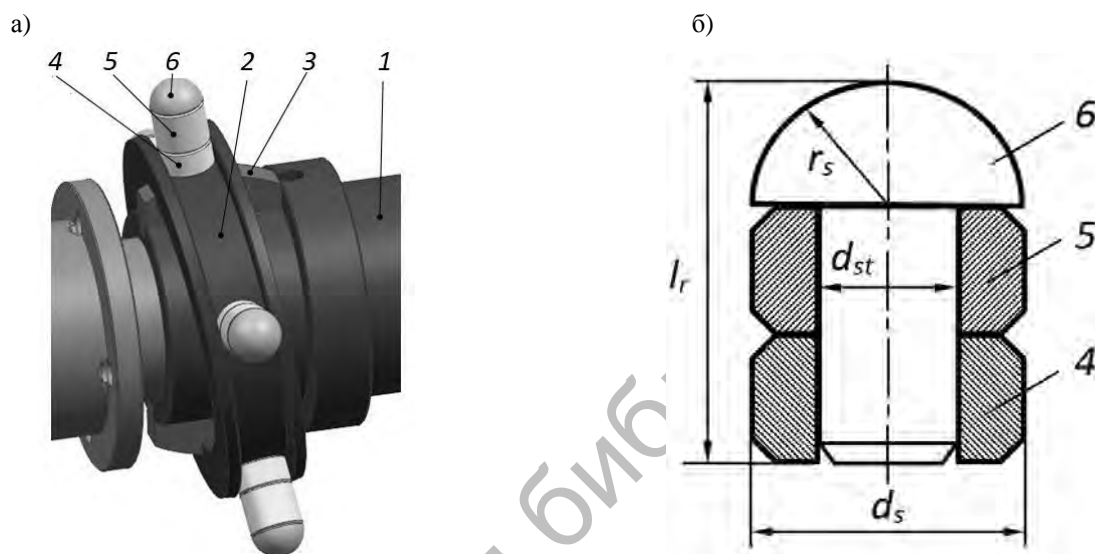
Ведущий и промежуточный элемент сферической передачи: а – общий вид ведущего элемента редуктора; б – схема составного промежуточного элемента; 1 – ведущий вал; 2 – внутренний кулачок; 3 – сектор; 4, 5, 6 – элементы составного ролика
